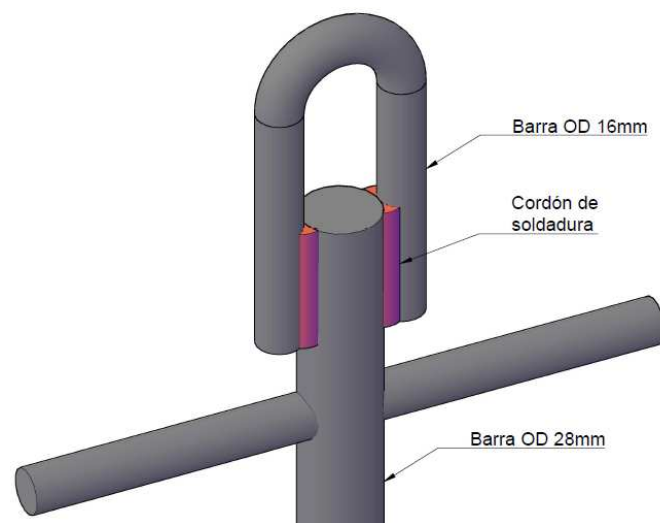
Perspectiva de unión soldada en extremo superior de la estructura entre barras de acero de OD 16mm y Barra de acero de OD 28mm.
